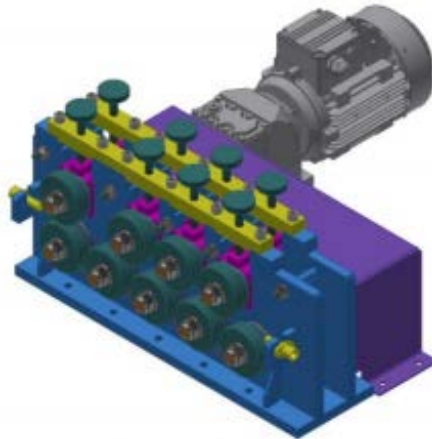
modèle CAD de dispositif de redressement de la machine réaliser.[26]
